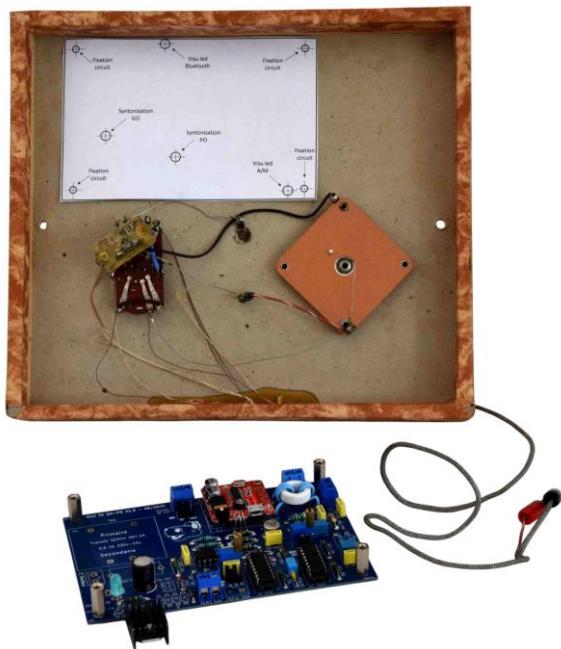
collage du gabarit de perçage à l’échelle 1, sur le fond de la face arrière.
